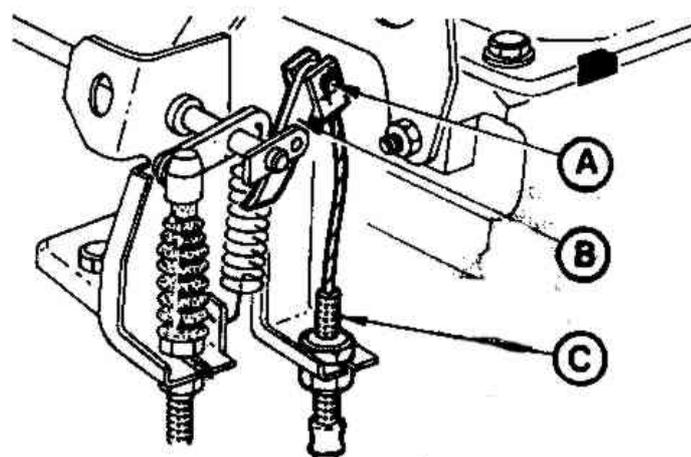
Штифт крепления троса понижения передачи (А), соединительный рычаг (В) и регулировочный узел (С) (Разд.13)
